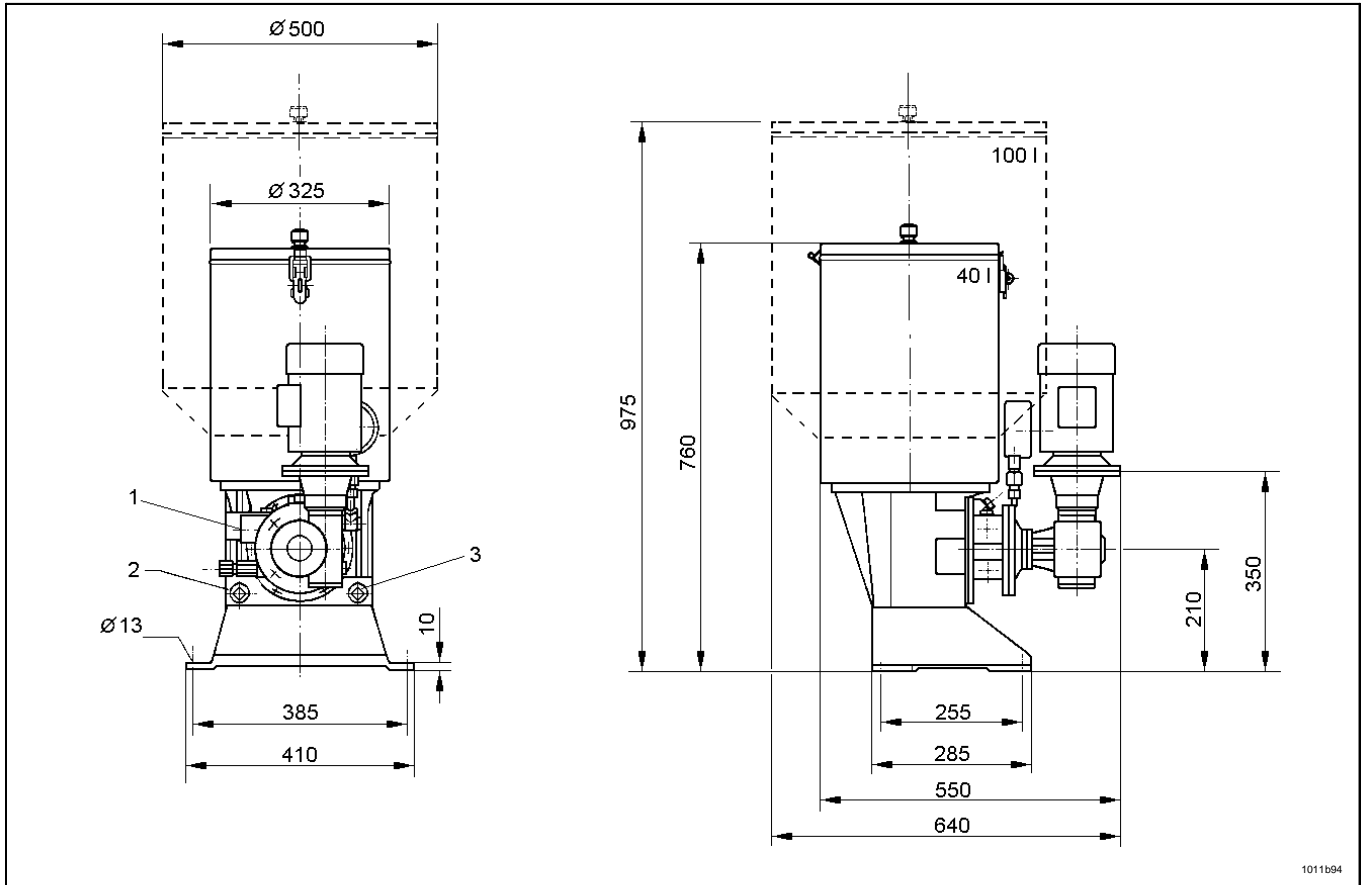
Abmessungen ZPU 08 S mit angeflanschem Schneckengetriebe
